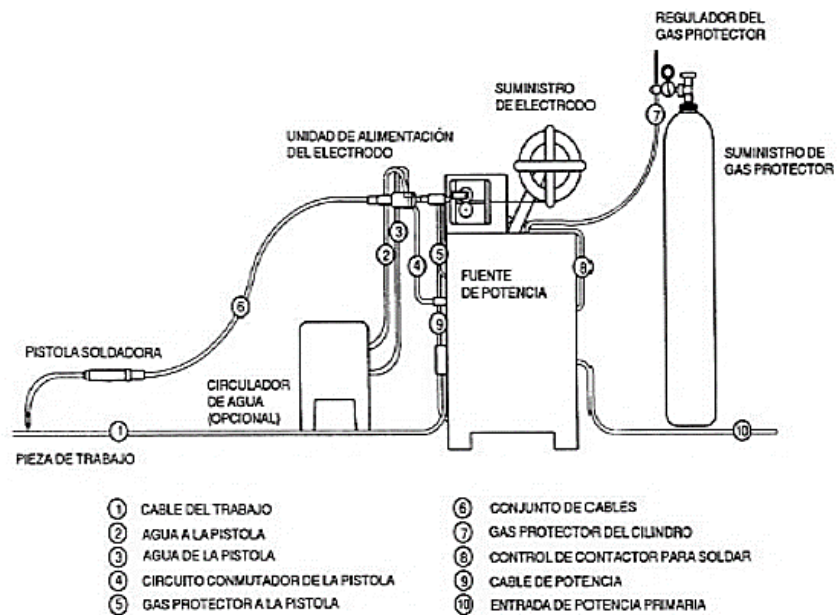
Equipo que se utilizan en soldadura GMAW [10].
